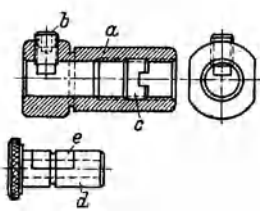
Einfacher Bohrerhalter, zum Einspannen von Bohrern, Senkern u. dgl. *a* Halterschaft; *b* Spannschraube zum Festspannen des Bohrers; *c* Anschlagsschraube zur Stützung des Bohrers; *d* Einsatzbüchse für kleinere Bohrerdurchmesser mit losem Druckstück *e*.
